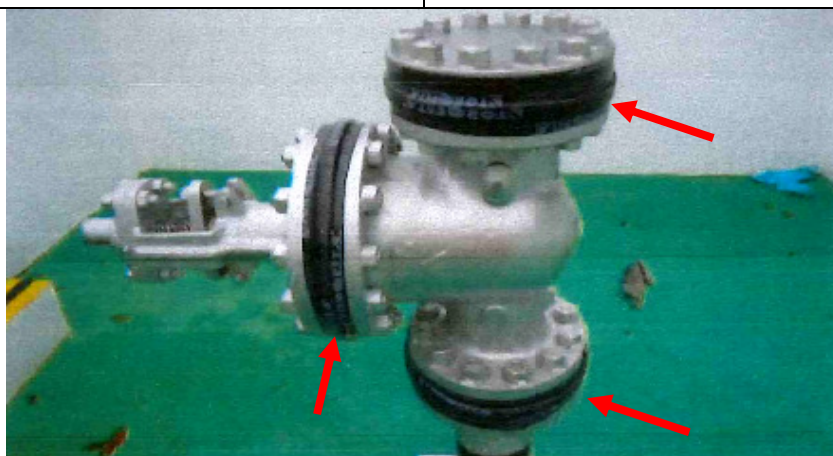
Juntas impermeabilizante entre os flanges e válvulas
